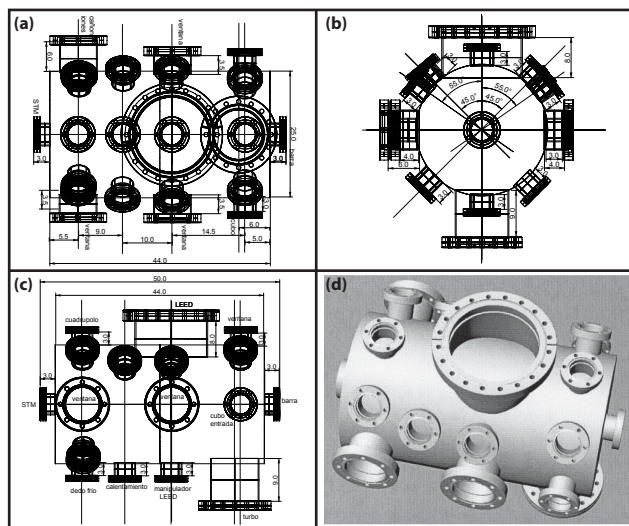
Planos de la campana de preparación diseñada en este proyecto. (a) Plano de la planta. (b) Plano de perfil. (c) Plano de alzado. (d) diseño en 3-D.
